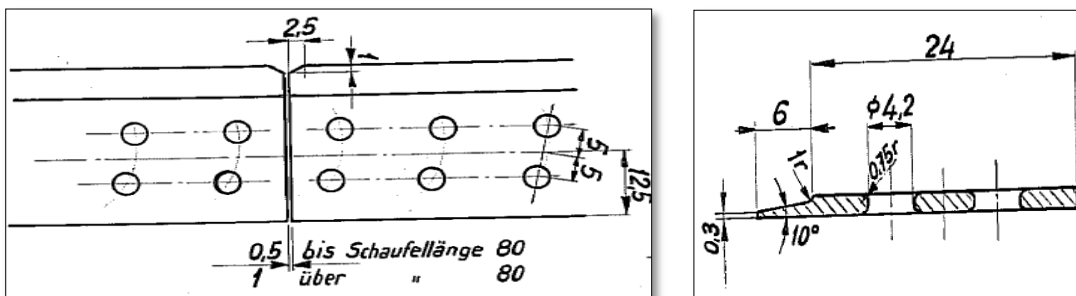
dimensioni del bendaggio del 7° stadio della macchina n° 3.
